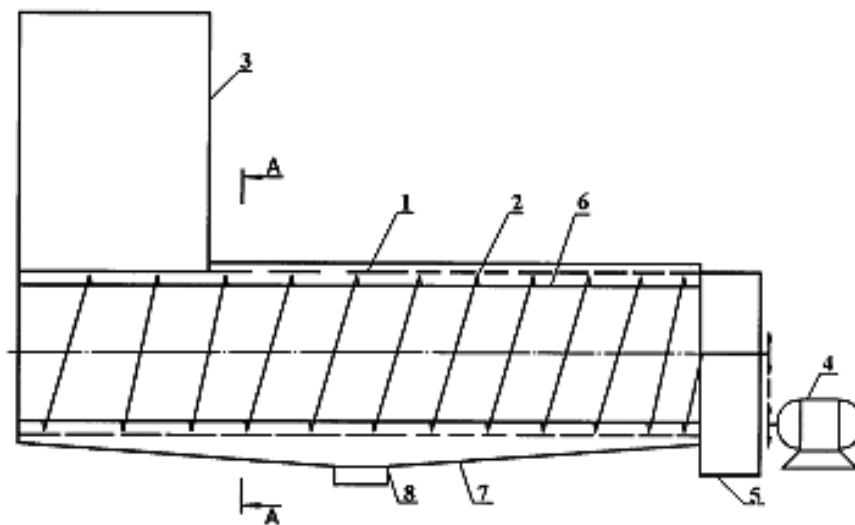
Установка для обезвоживания птичьего помета: 1- корпус, 2- спирально-винтовой рабочий орган, 3- загрузочный бункер, 4- привод, 5 – выгрузной патрубков, 6- стакан, 7-кожух, 8 - сливной патрубков.
